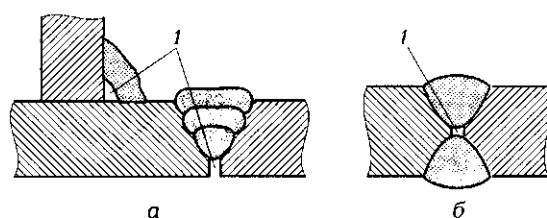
Непровар (1) корня углового и стыкового односторонних (а) и стыкового двустороннего (б) сварных швов
